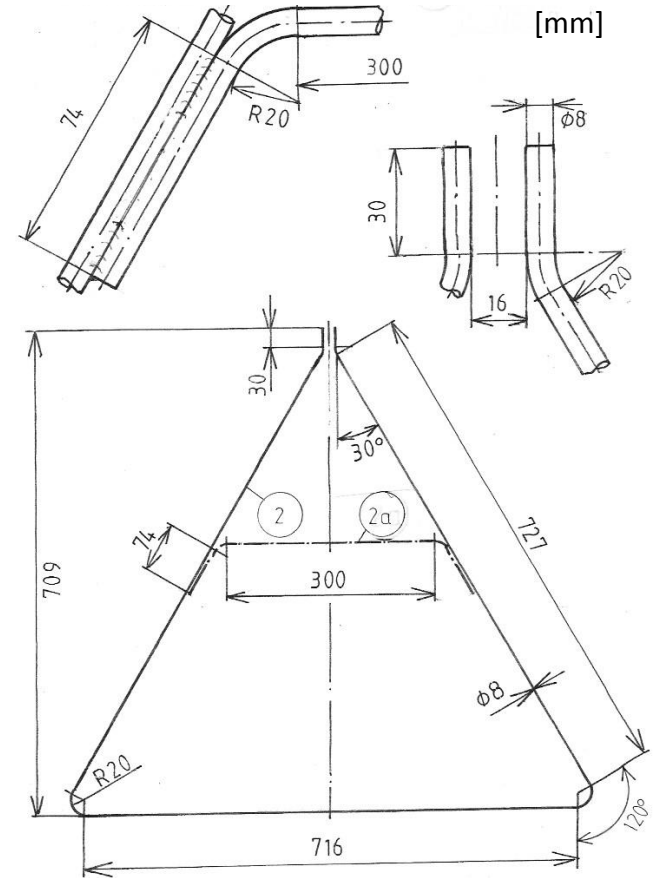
Puntal vertical (2) con traviesa (2a) soldada al puntal; puntal con traviese en un plano
